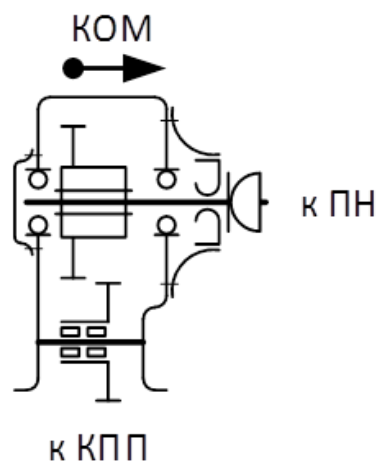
Кинематическая схема коробки отбора мощности, устанавливаемой к приводному валу через зубчатую передачу
